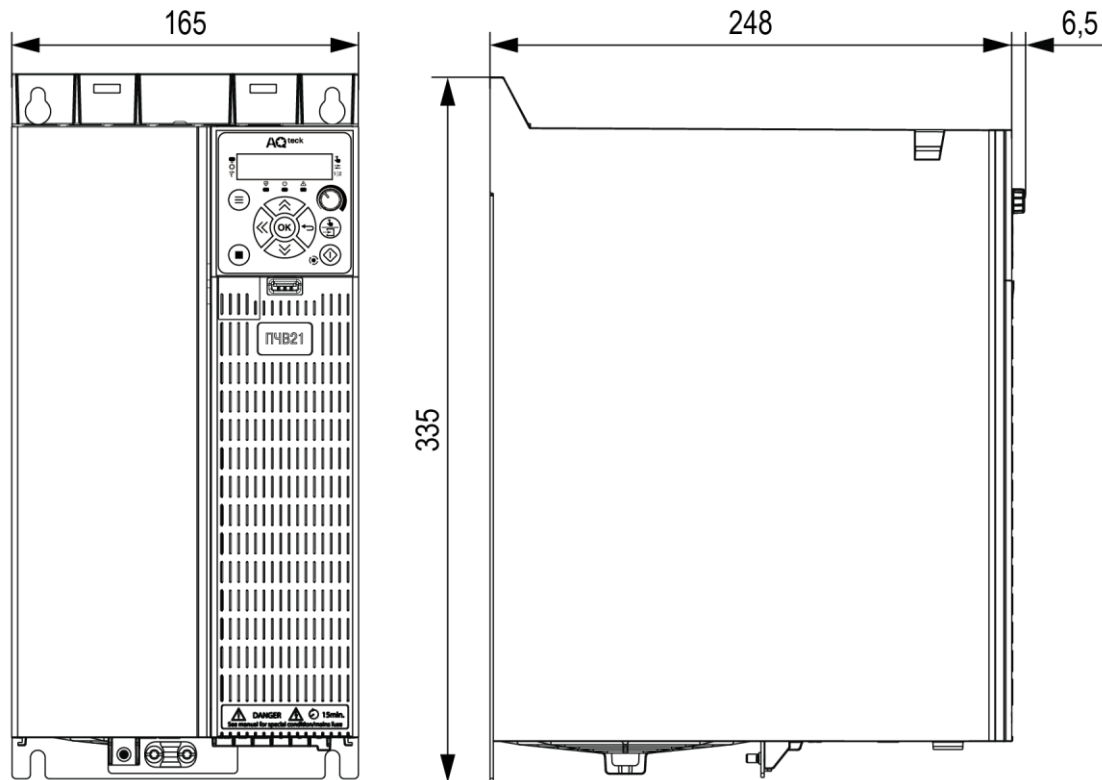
Габаритні розміри ПЧВ у корпусі 7
